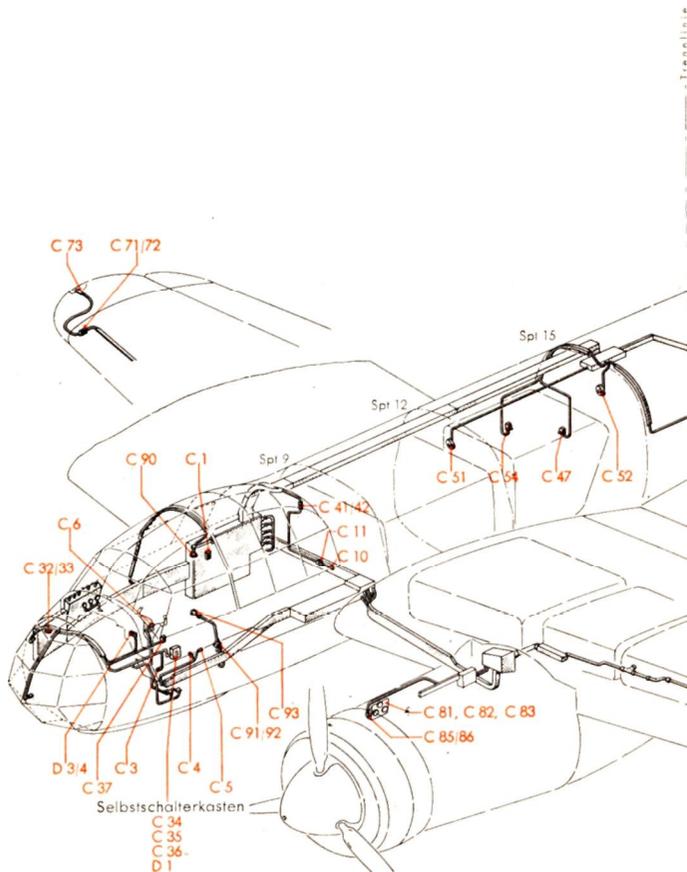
Lageplan der Beleuchtungs- und Staurohrheizungsanlage
